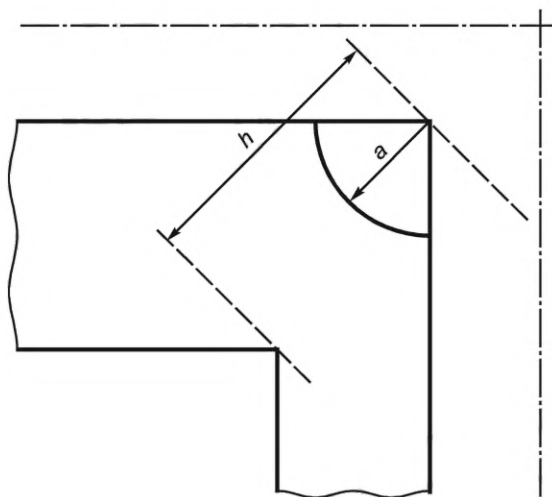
Схема расположения трещины по образующей цилиндра
